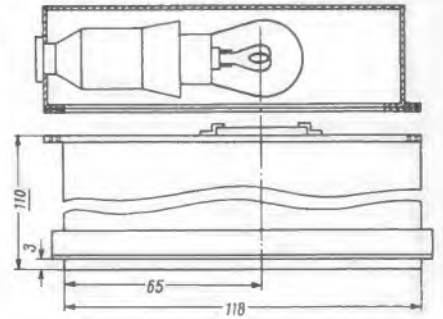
Lampengehäuse mit Umrandung, zwei Dichtungen, Mattscheibe, Papierfenster und Fassung mit Glühlampe
